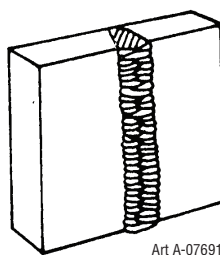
Position verticale, soudure par aboutement
